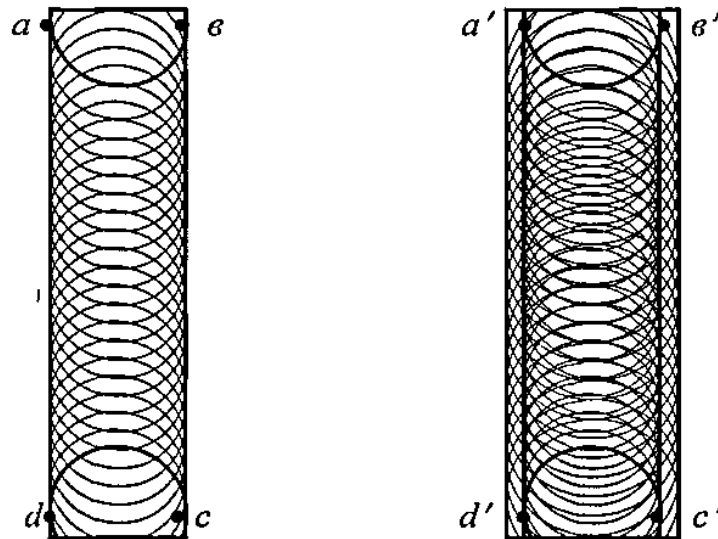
Схемы обработки изделия одним и двумя абразивными кругами за один проход
